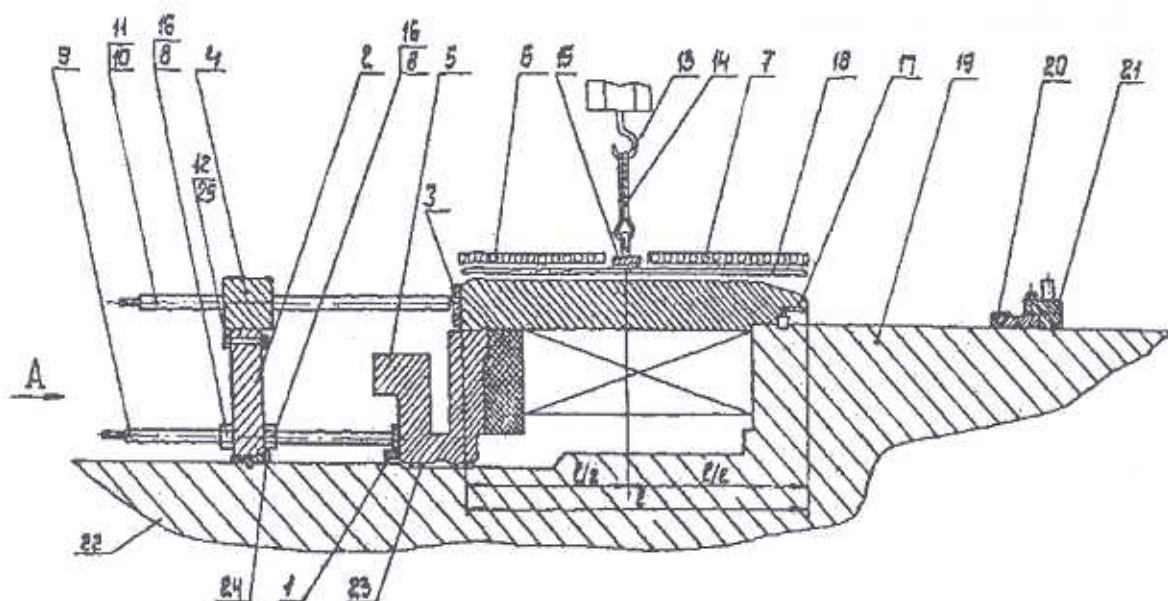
Установка приспособлений и надевание бандажного кольца на ротор:
